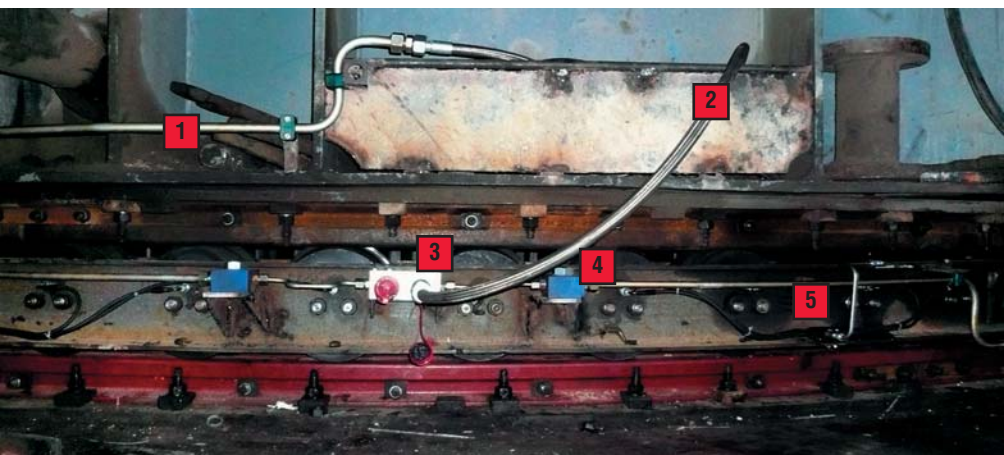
Полуавтоматическая смазка подшипников роликов опорно-поворотного круга:
